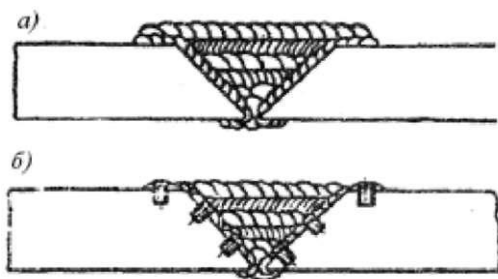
Вид стыкового соединения чугуна: а - стальнение поверхности без установки шпилек; б - стальнение поверхности с установкой шпилек
